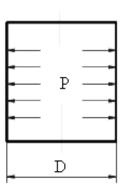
Расчетная схема цилиндрической обечайки
